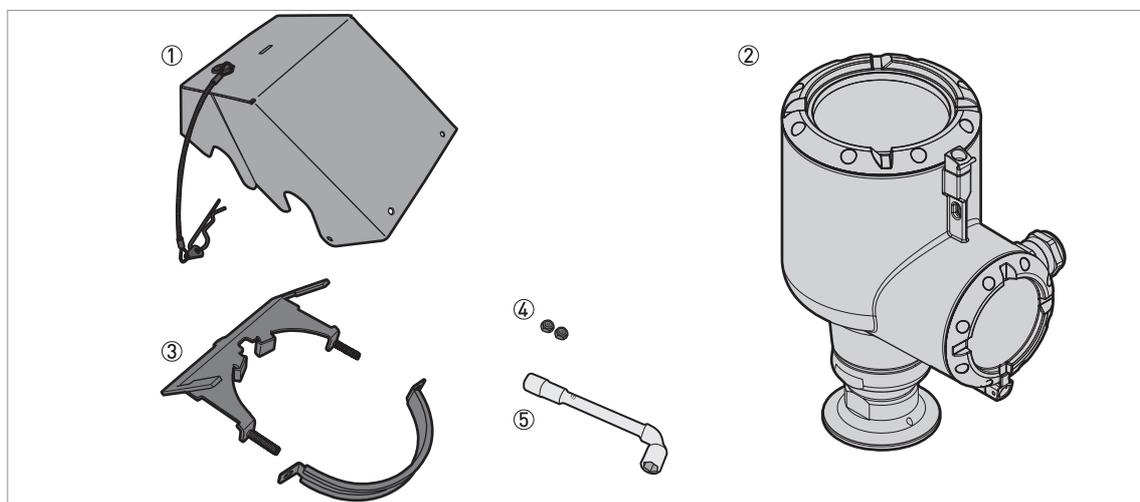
Оборудование, необходимое для сборки защитного козырька
